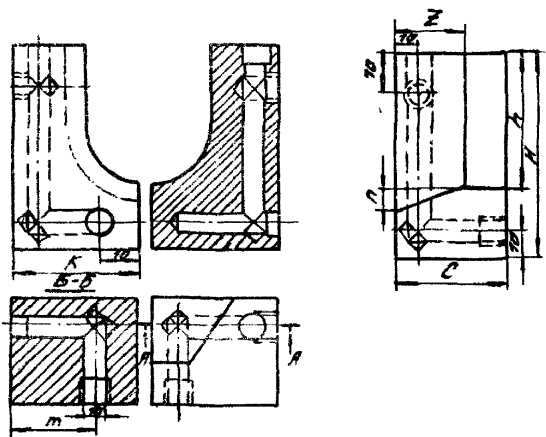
Рабочие чертежи медных форм для сварки втавр одиночных стержней с пластиной при изготовлении закладных деталей типа "открытый" и "закрытый" столик.
